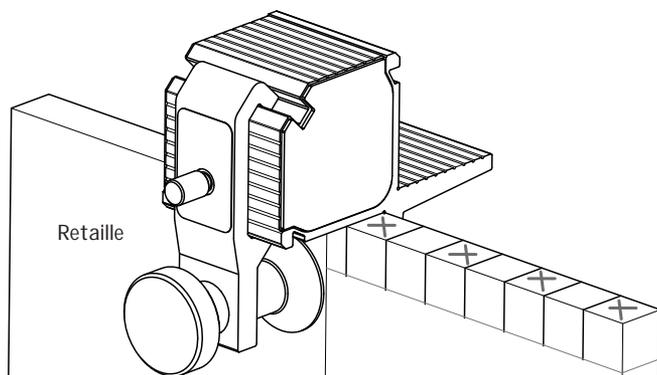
Juxtaposition d'une retaille de bois à la pièce à travailler pour stabiliser le guide pendant la coupe des dernières entures
